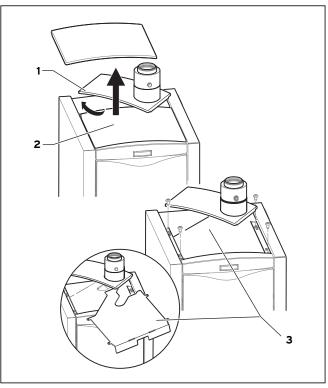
Retrait de la plaque de protection et de recouvrement
